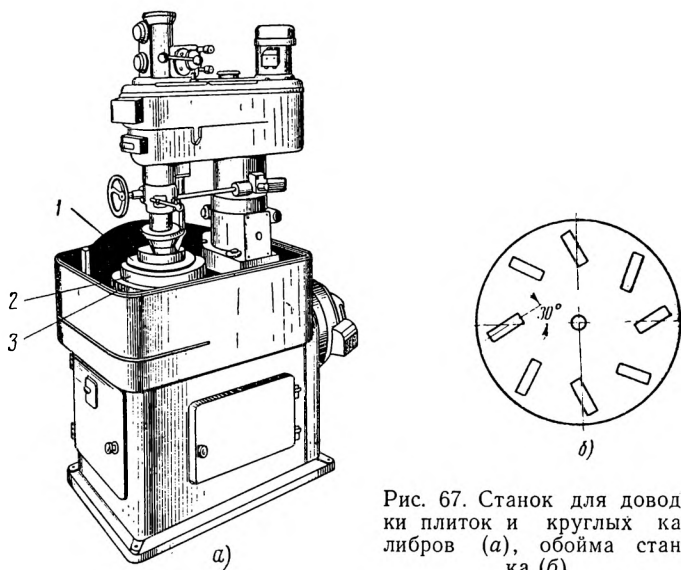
Станок для доводки плиток и круглых калибров (а), обойма станка (б)
